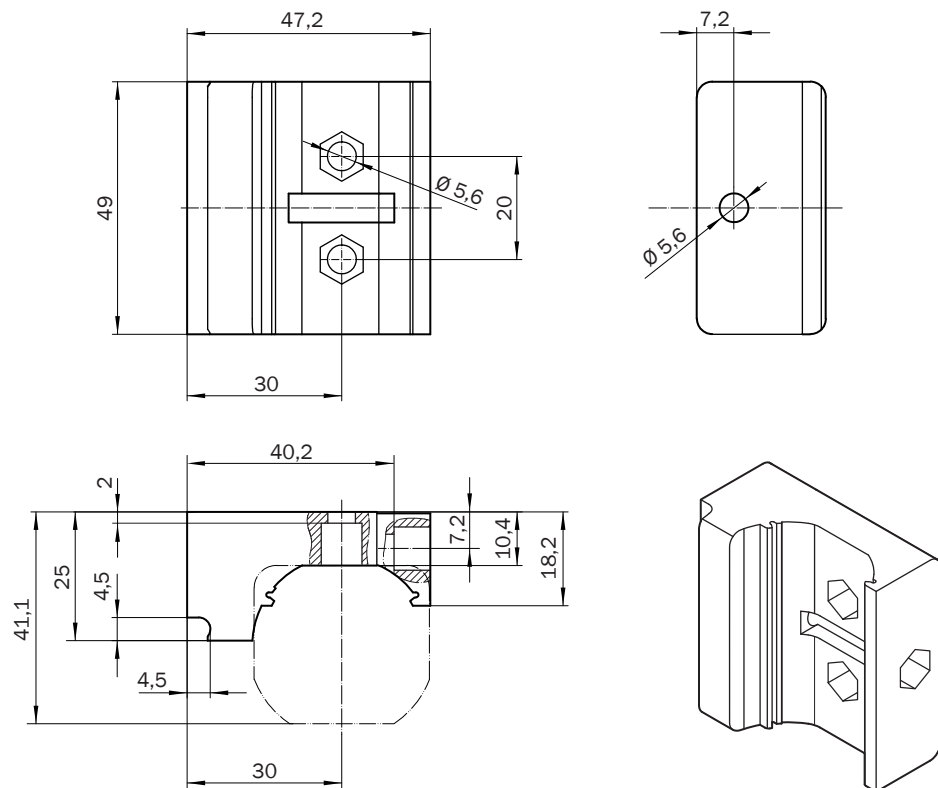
Plan coté de la fixation QuickFix (2066048)
